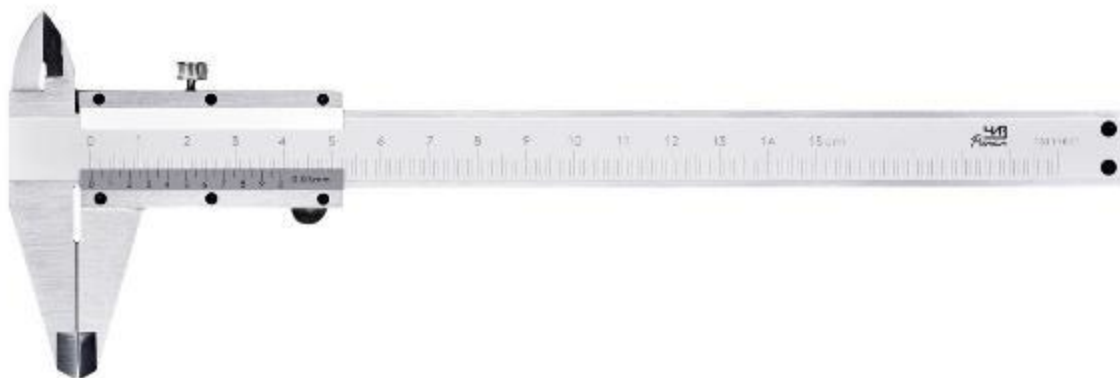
Общий вид штангенциркулей ШЦ-I
